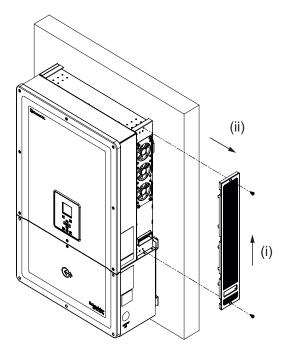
Retrait du couvercle de la grille d'aération – Côté gauche
